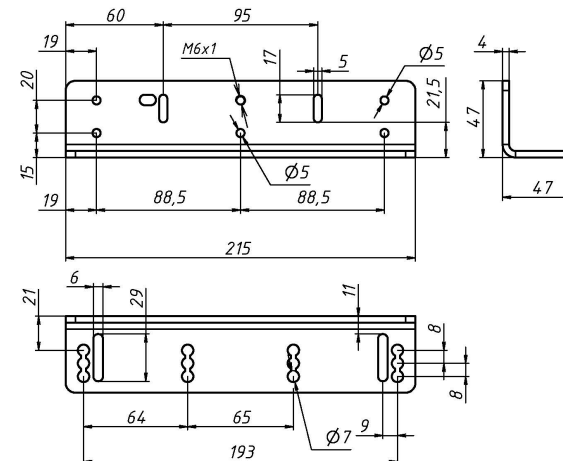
L-уголок AL-350FB-M Габаритный чертеж
